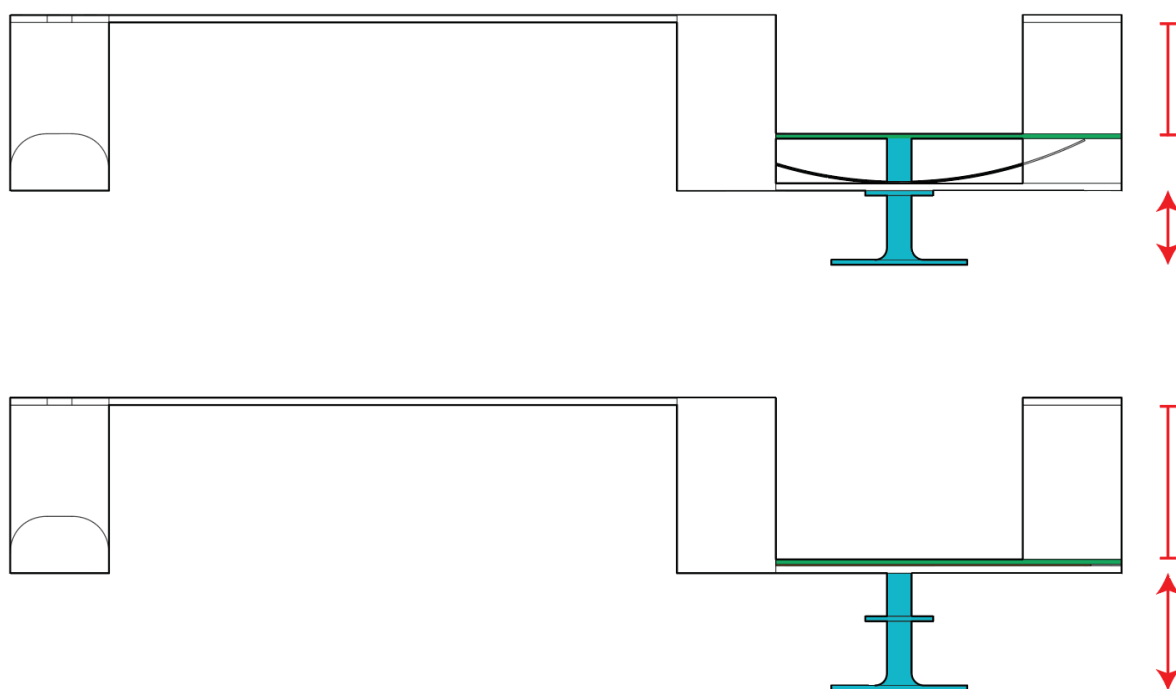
Dimostrazione movimento e regolazione del Concept 4 in vista dall'alto
